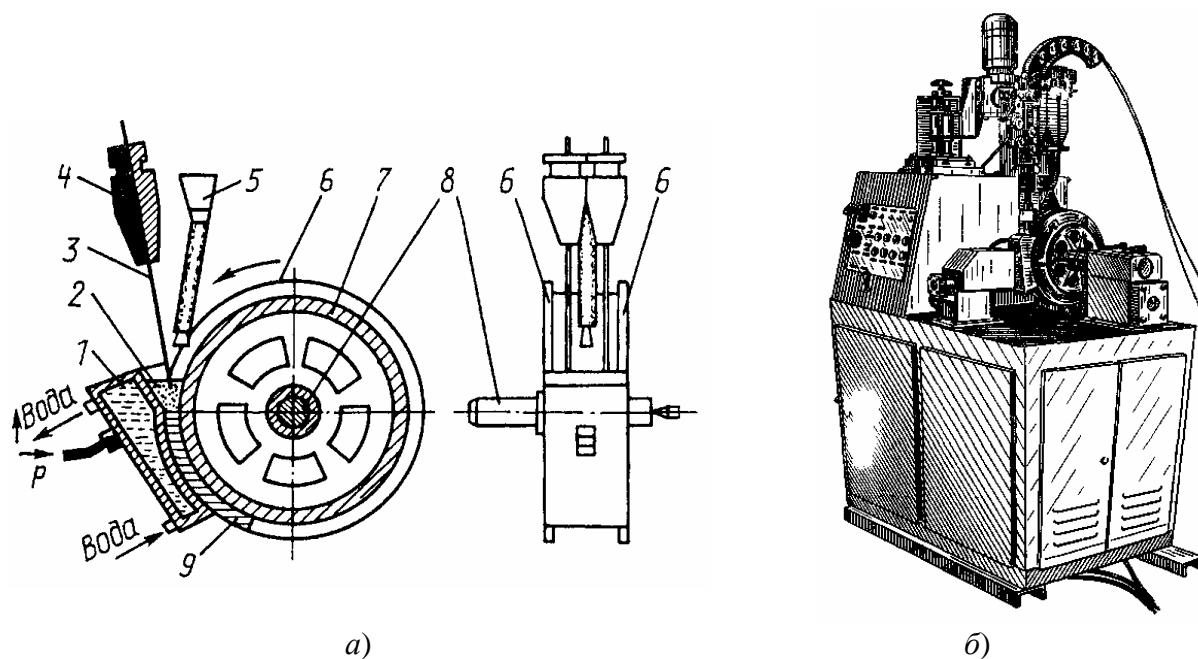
Схема и общий вид установки ОКС-7755 ГОСНИТИ для электрошлаковой наплавки катков и шкивов: *а* – схема процесса; *б* – общий вид; 1 – кристаллизатор; 2 – шлаковая ванна; 3 – электрод; 4 – мундштук; 5 – дозатор легирующих добавок; 6 – габаритные диски; 7 – восстанавливаемая деталь; 8 – оправка; 9 – покрытие
